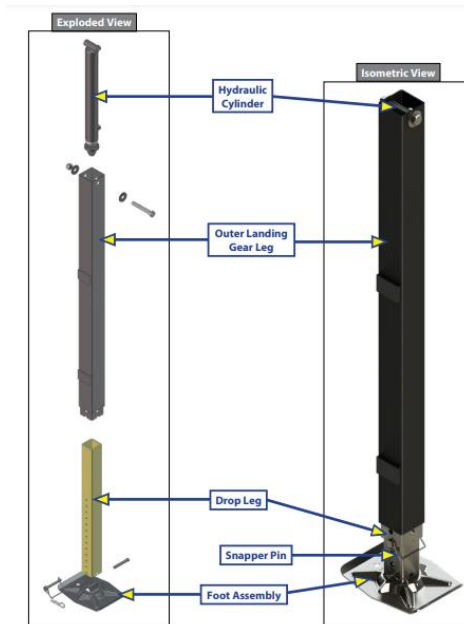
Despiece de un gato hidráulico Fuente: Lippert.com
